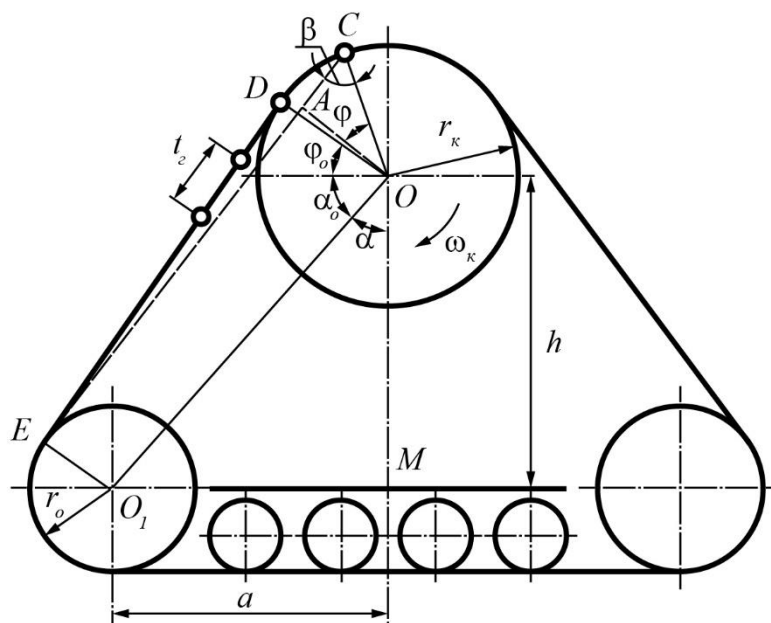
Схема гусеничного рушія трикутної форми з верхнім розташуванням ведучої зірочки
